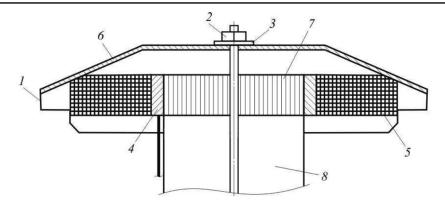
Воздухозаборный колпак: 1 – колпак; 2 – крепежная гайка; 3 – шайба; 4 – электронагреватель; 5 – сетка; 6 – термооболочка; 7 – фильтр
